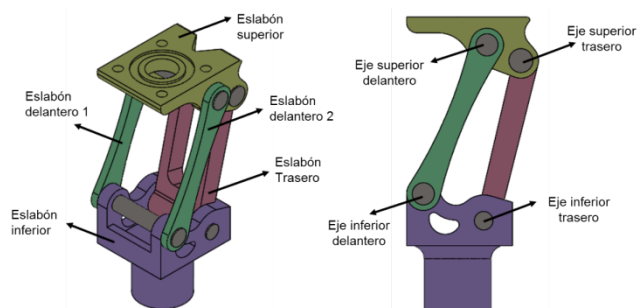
Componentes de la prótesis de rodilla policéntrica.
